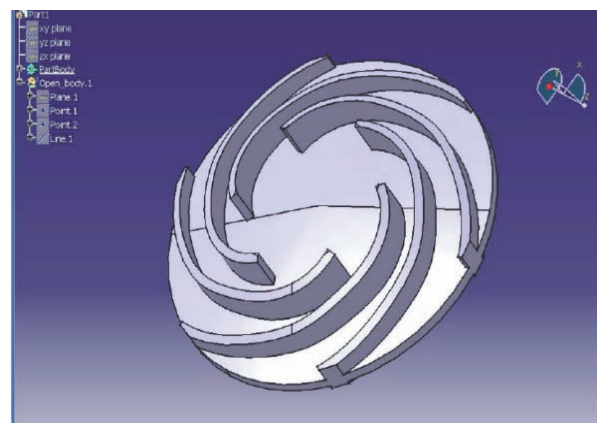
Rotor modelado a partir de sus dimensiones básicas
